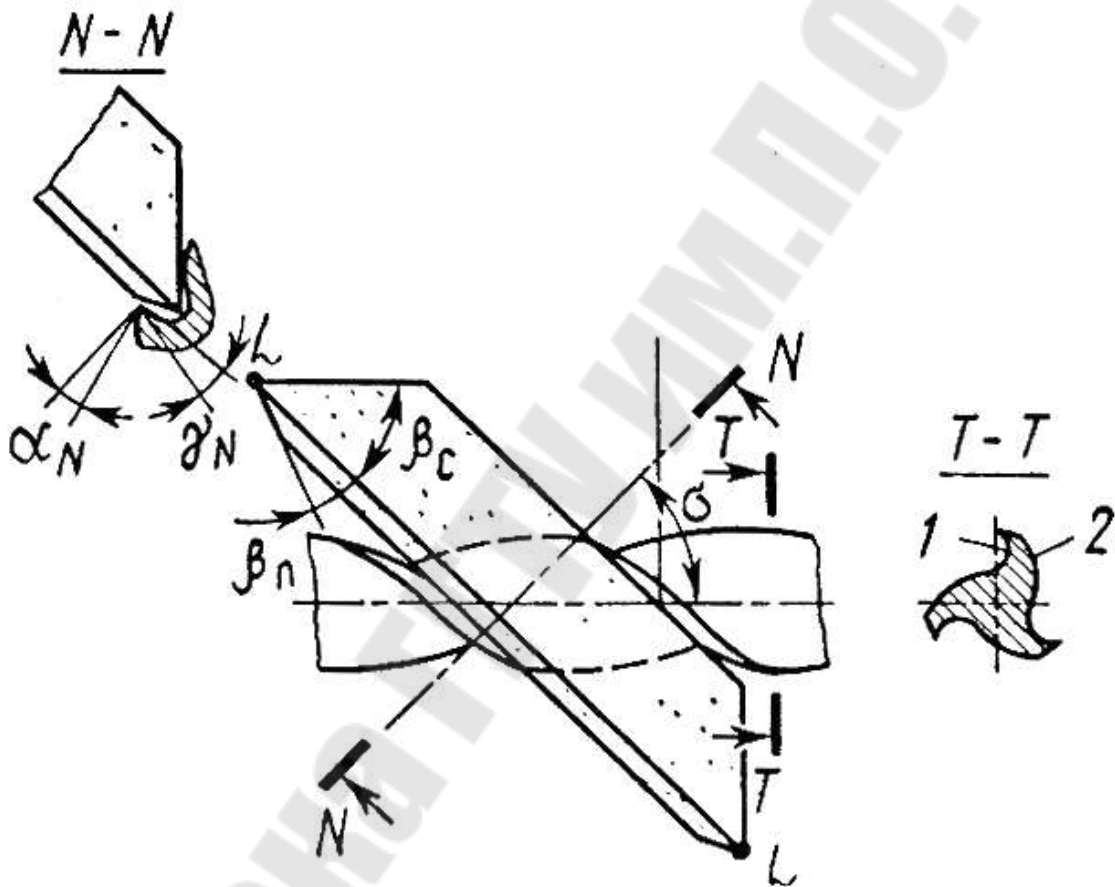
Схема расположения концевой фрезы и абразивного инструмента при вышлифовке винтовых канавок: 1 – передняя поверхность; 2 – спинка
